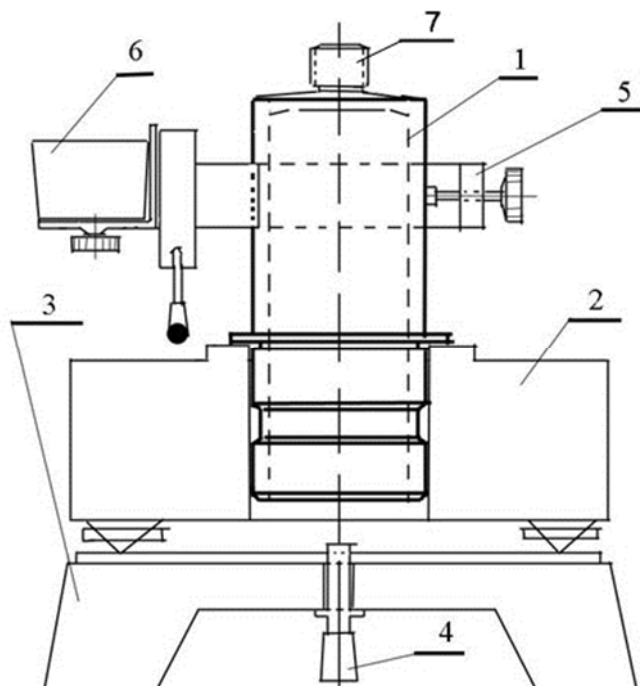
Схема крепления лазерного дальномера к геодезическому штативу: 1 – адаптер трегера; 2 – трегер; 3 – штатив; 4 – становой винт; 5 – адаптер LSA-360; 6 – лазерный дальномер; 7 – винт для GPS
